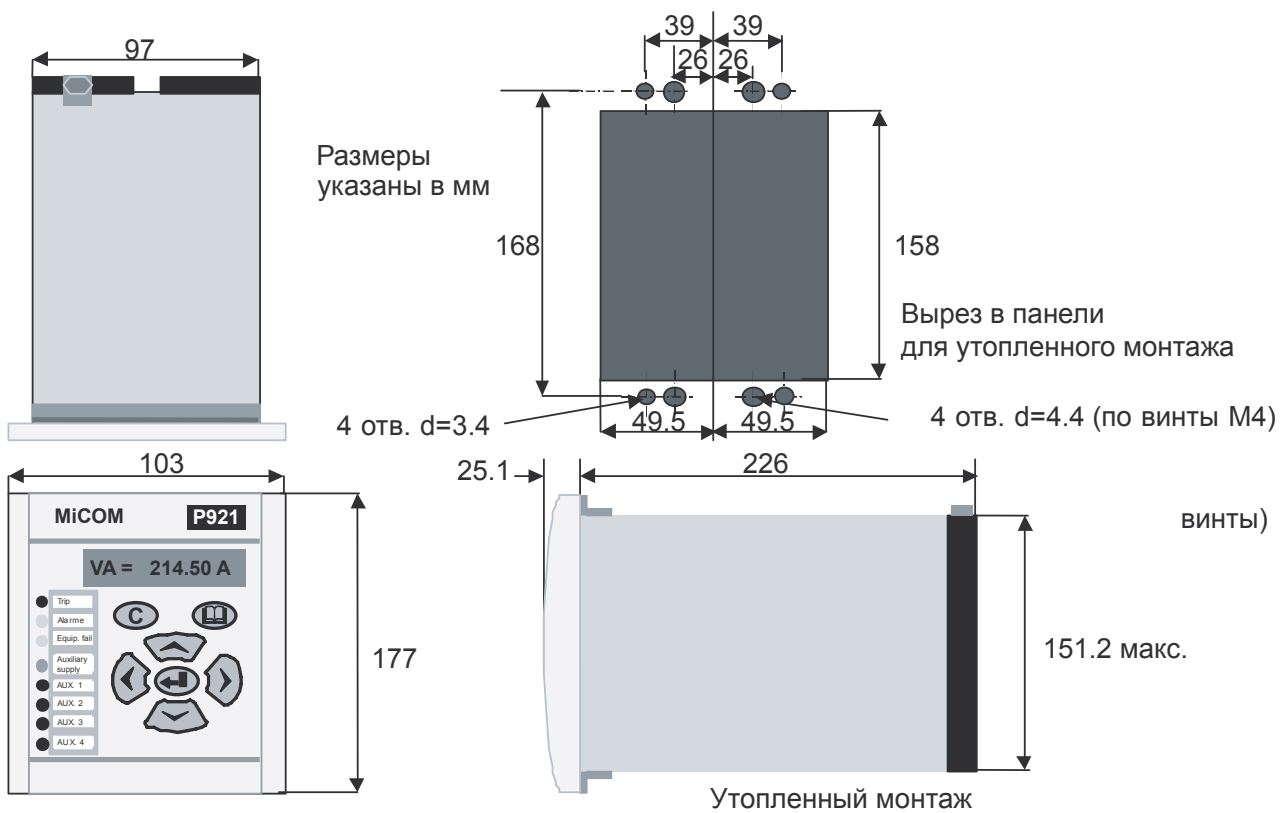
Габаритные размеры корпуса реле MiCOM P921-P922
